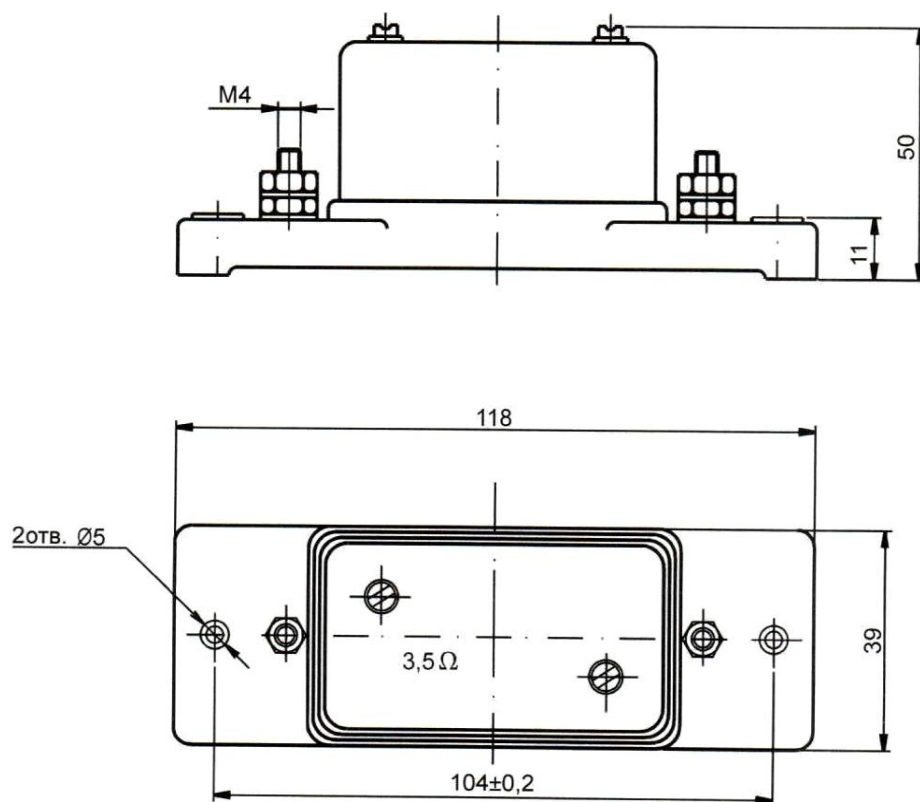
Габаритный чертеж резистора подгоночного Р1830
